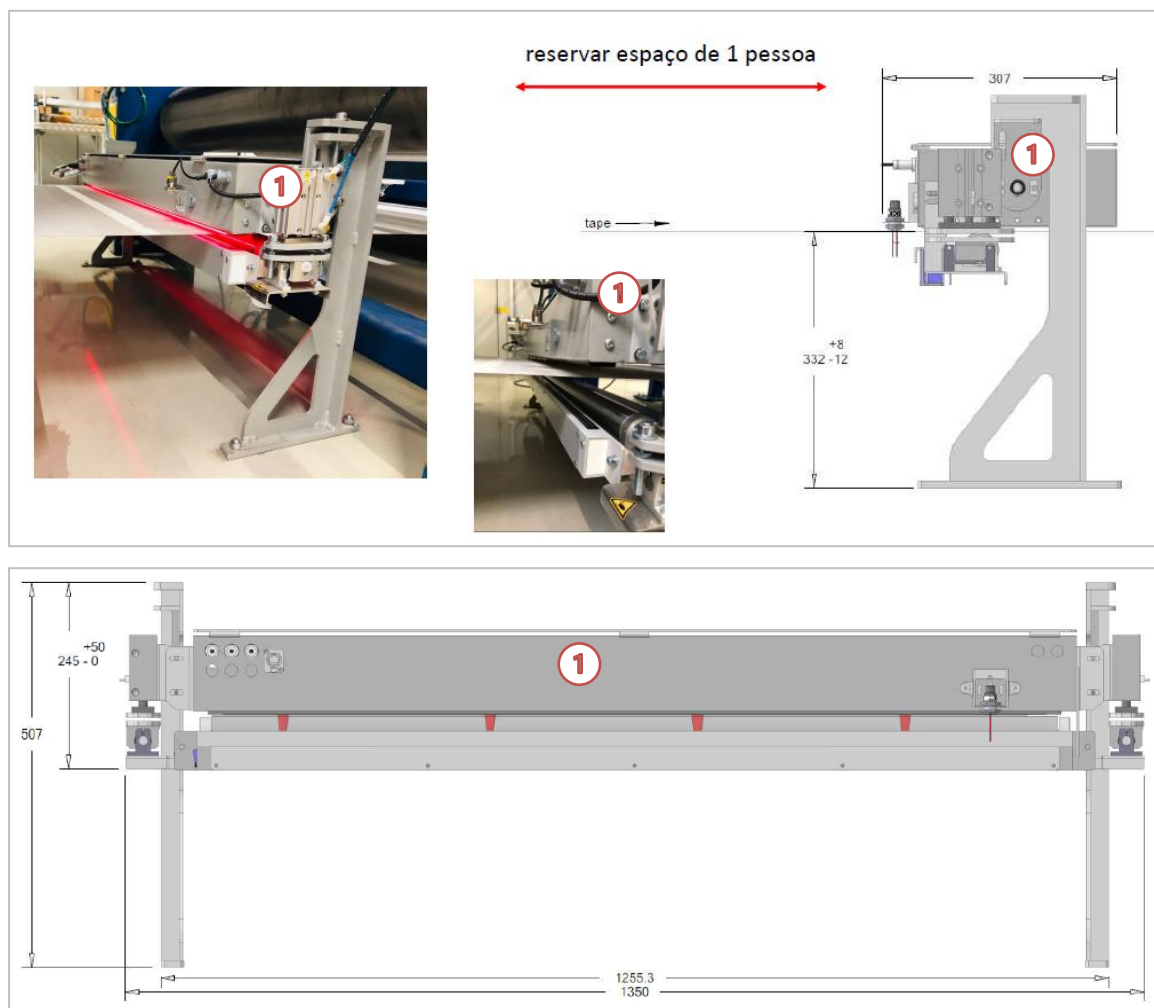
Fotos e desenhos técnicos da caixa de sensores e suas dimensões
